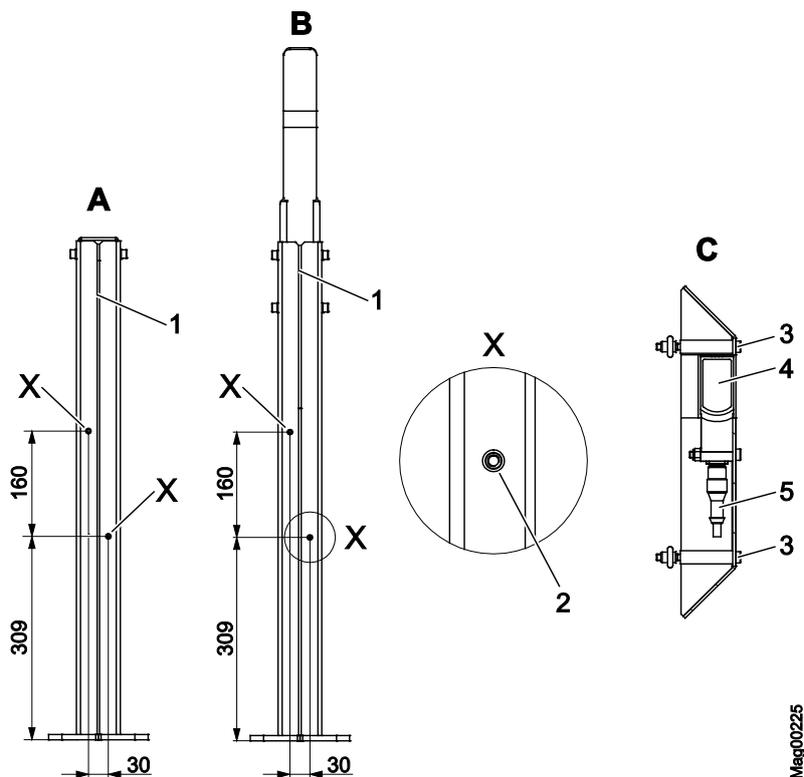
Lichtschrankengehäuse des Empfängers am Pfosten montieren
